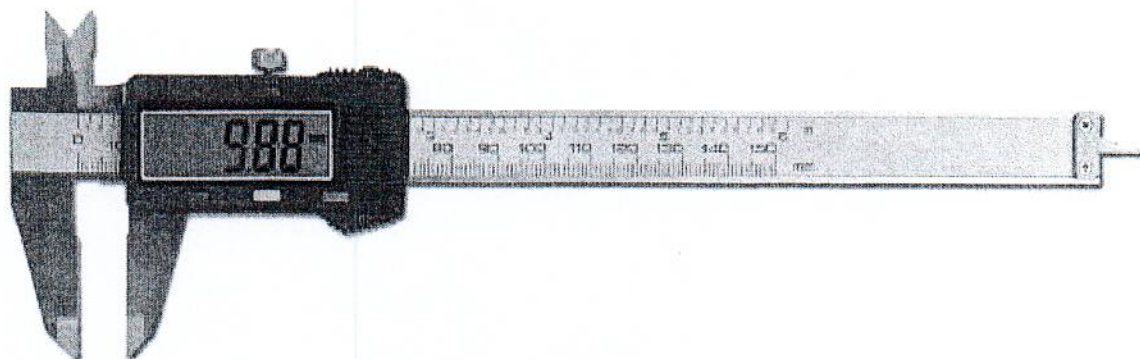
Внешний вид штангенциркуля типа ШЦЦ-I
